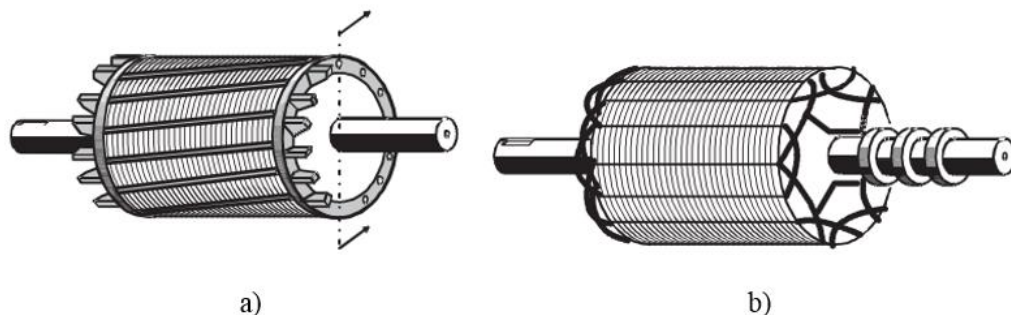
a) Rotor tipo jaula de ardilla, b) rotor devanado [26].
